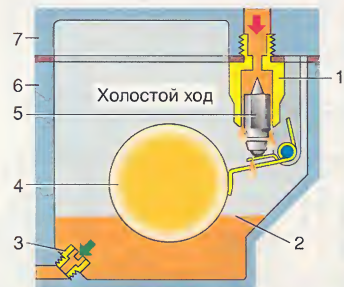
Схема поплавковой камеры: 1 — игольчатый клапан; 2 — уровень топлива; 3 — главный топливный жиклер; 4 — поплавок; 5 — игла; 6 — корпус; 7 — крышка.
